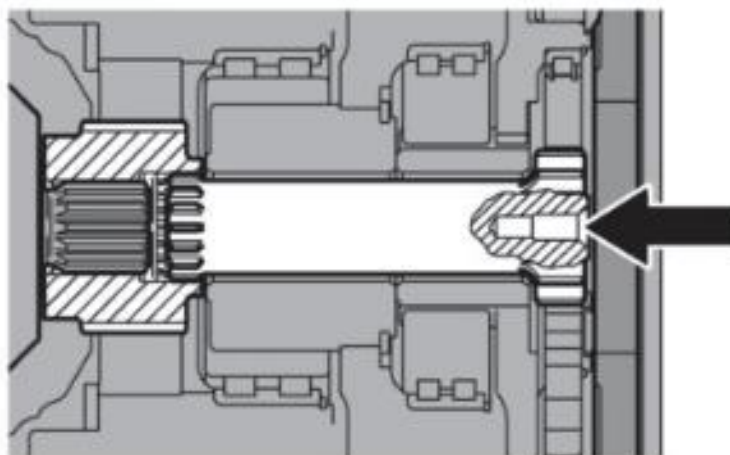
Резьбовое отверстие в шлицевом вале
